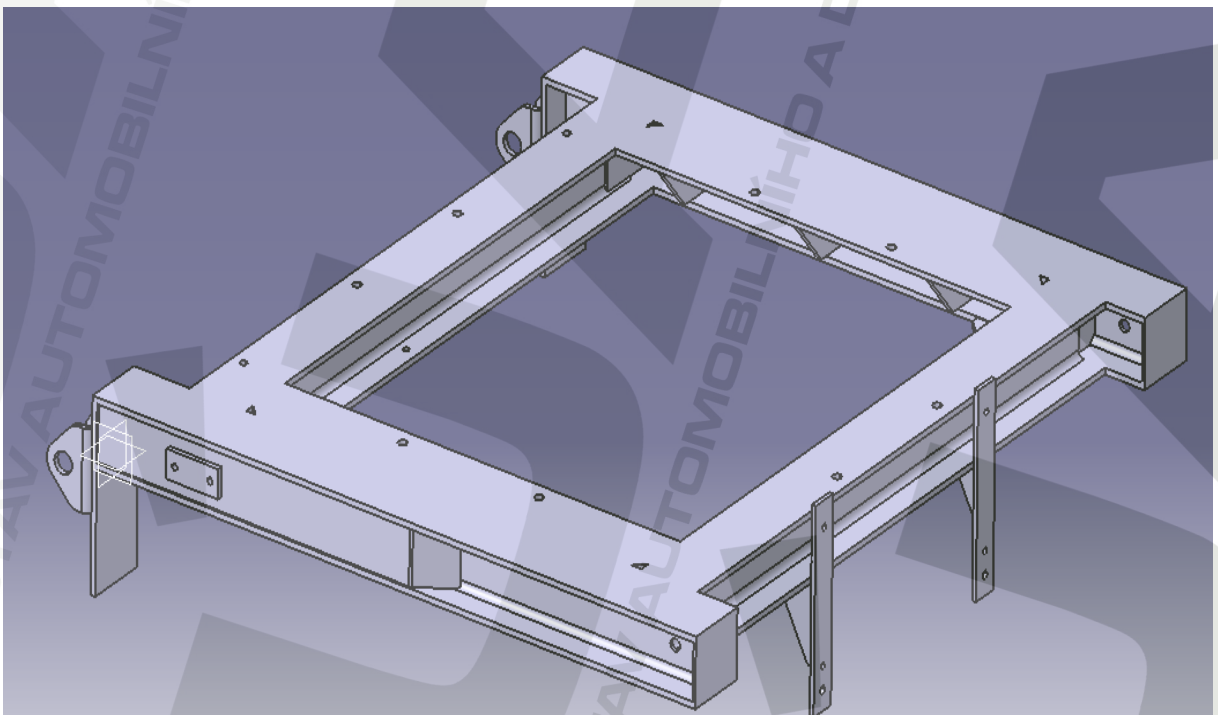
; Přední část hlavního rámu – uložení točnice
